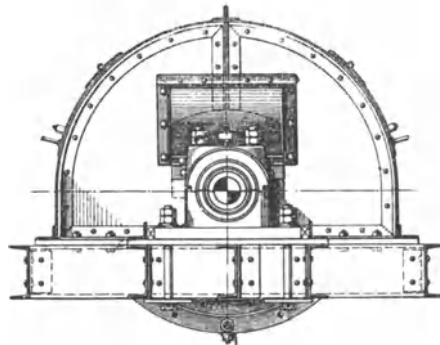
Schleudermühle oder Desintegrator (Humboldt).
